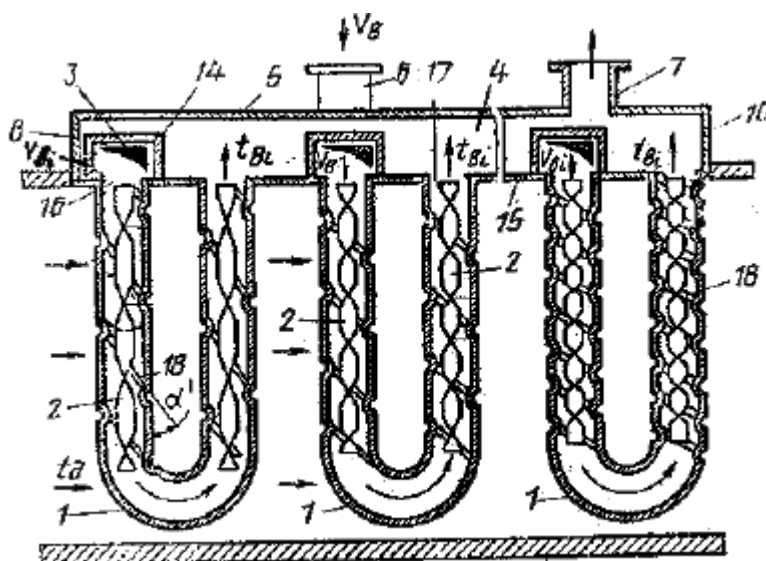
U образный теплообменник: 1– U - образная труба; 2 – закрученная вставка; 3– воздушный короб; 4 – короб нагретого воздуха; 5 – крышка; 6 – подводящий патрубок; 7 – отводящий патрубок; 8, 9, 10, 11– боковые стенки; 12– разделительная стенка; 13– отверстия; 14 – П-образная раздаточная труба; 15 – распределительная пластина; 16, 17– впускное и выпускное отверстие; 18 – многозаходные спиральные выступы.
